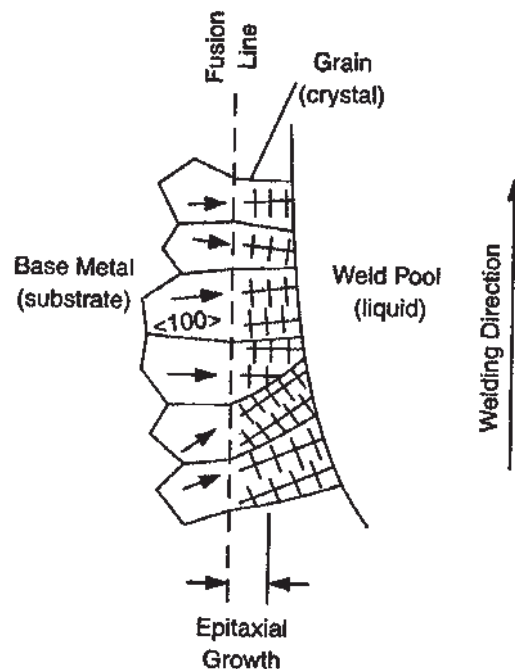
Crecimiento epitaxial del metal de soldadura próximo a la línea de fusión.
